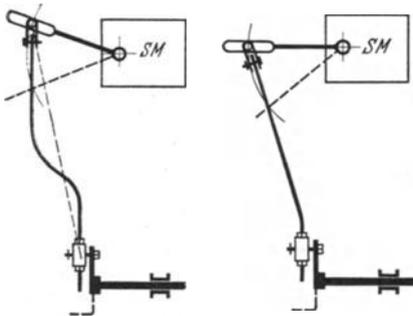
Guter und schlechter Zugstangenantrieb für Schäfte.
